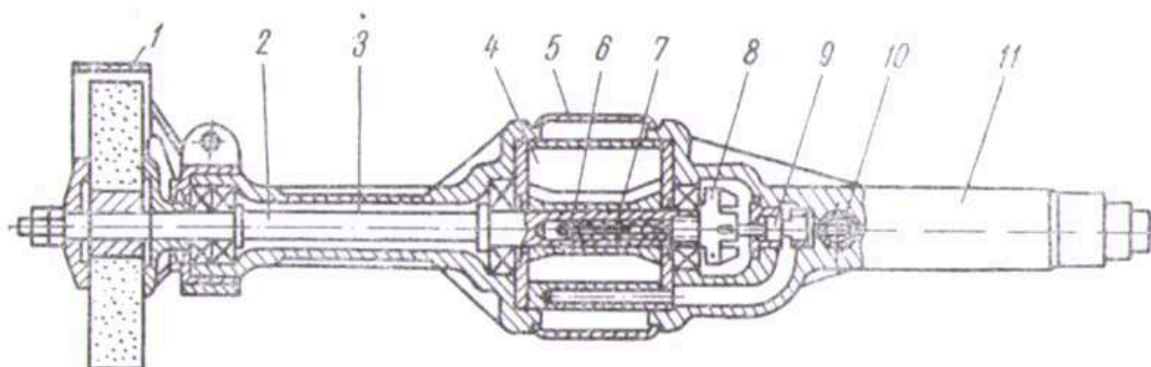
Řez dopravní jednotkou poháněnou pneumatickým motorem
